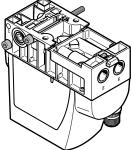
Befestigung über Seitenfläche mit innenliegenden Schrauben M4/ durchgehenden Schrauben M4
